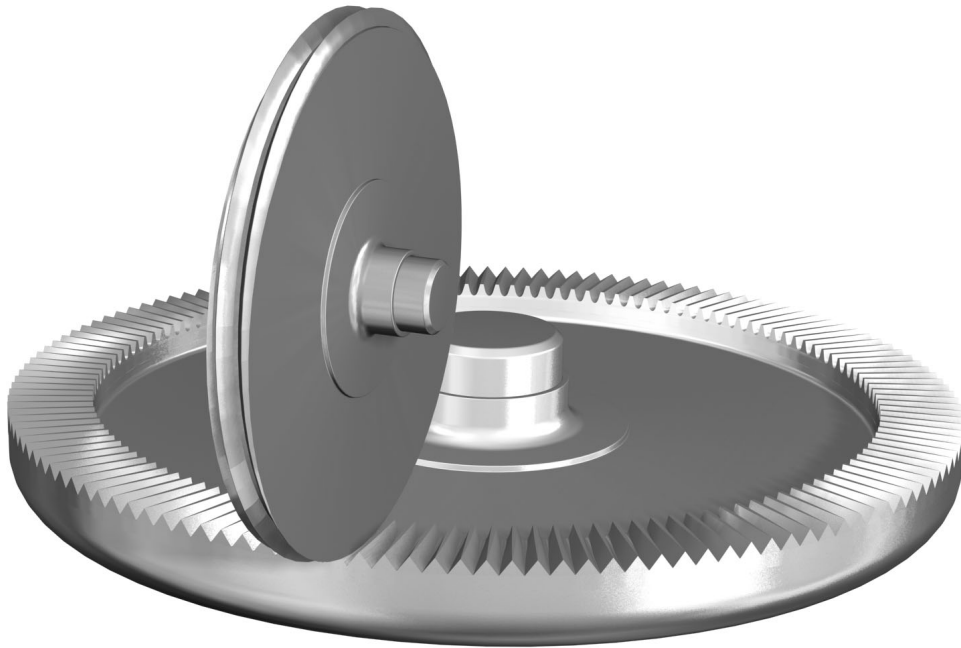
Ilustración del engrane entre el engranaje de cara y el cortador sinfín.
